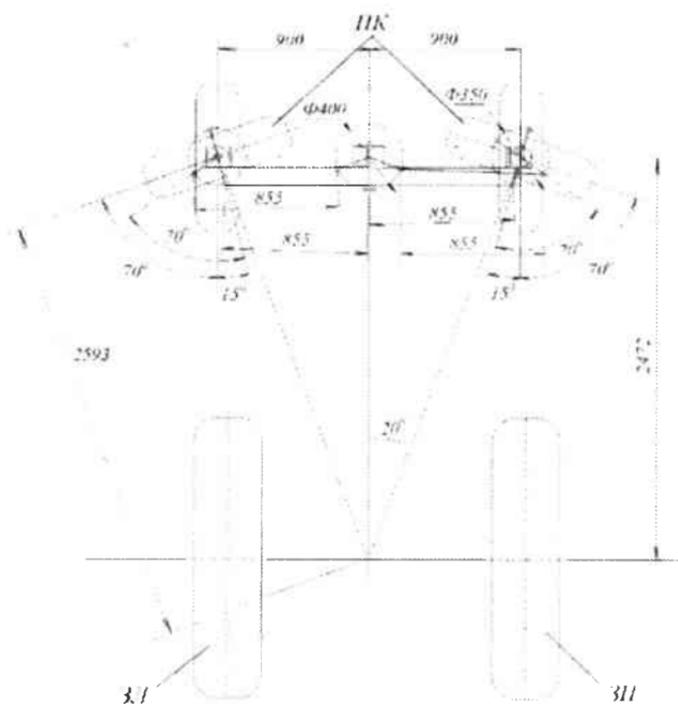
Схема поворота направляющих колес при разворотах вокруг центра заднего моста
